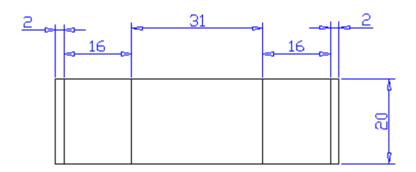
MEDIDAS PRIMER CUERPO PARA TANQUE PRINCIPAL A SER DOBLADO FUENTE: LOS AUTORES
